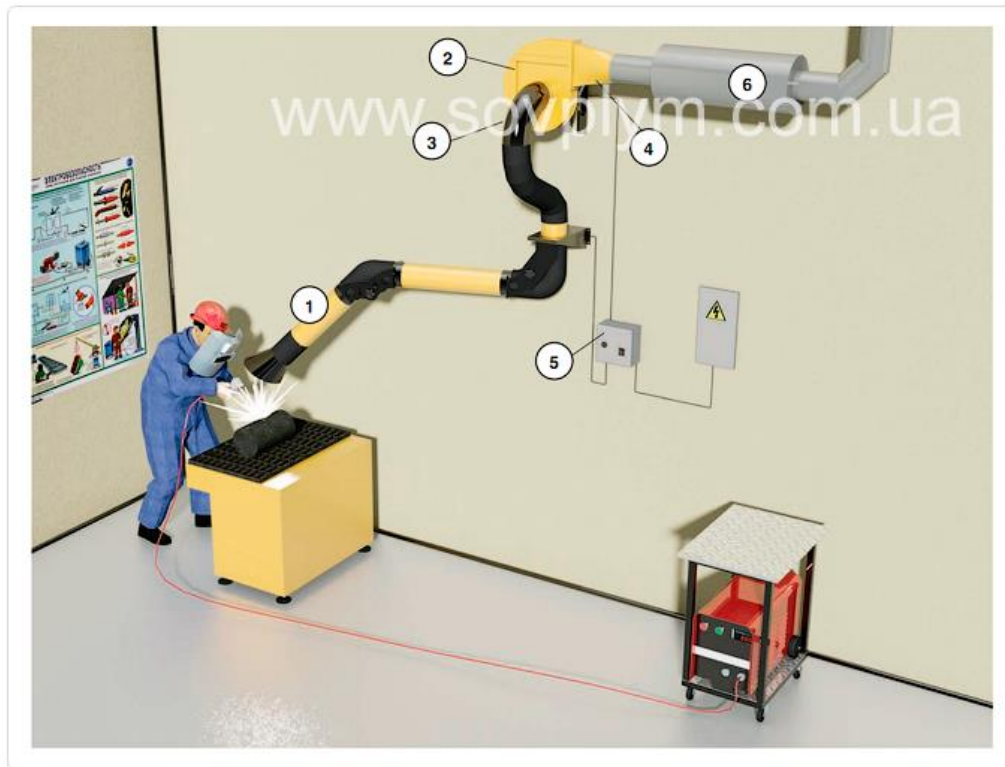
Загальна компоновка витяжки робочого місця зварювальника
